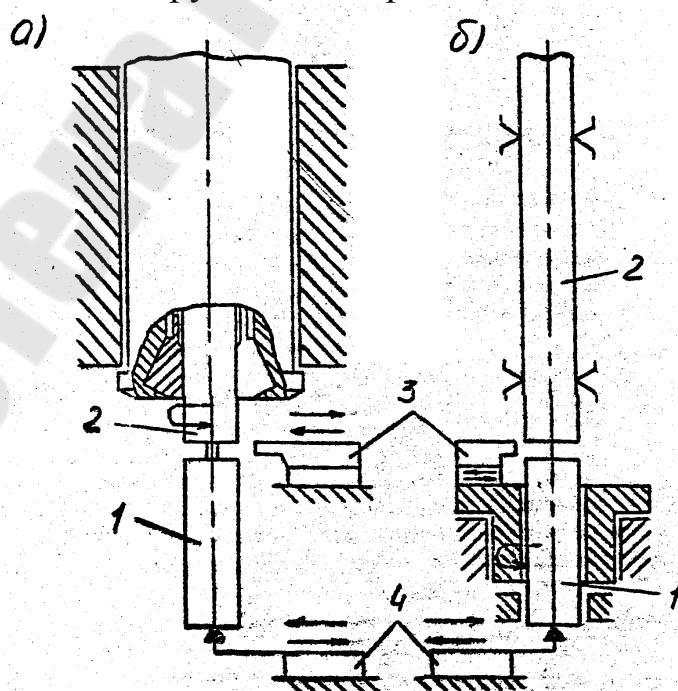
Принципиальные схемы токарной резки на станках: а) с вращающимся прутком; б) с вращающимся резцом; 1 – отрезанная заготовка; 2 – разрезаемый пруток; 3 – отрезной резец; 4 – подвижный упор
